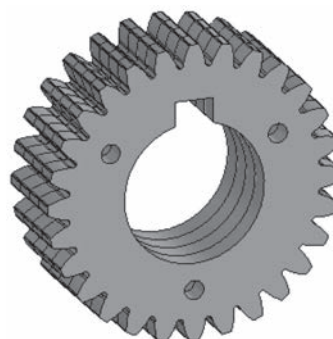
3D-модель цилиндрической шестерни в сборе
